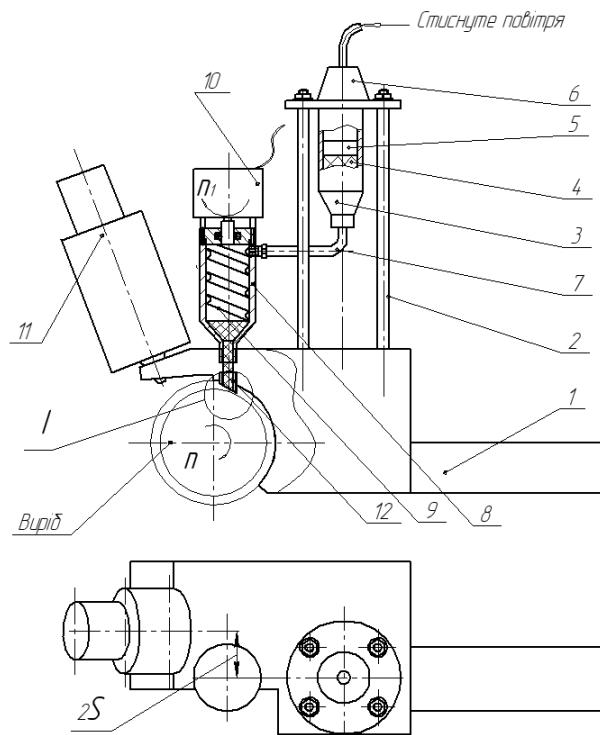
Пристрій для нанесення на різбову поверхню легкоплавкого сплаву: 1 – оправка; 2 – стійка; 3 – система подачі; 4 – паста-припой;
